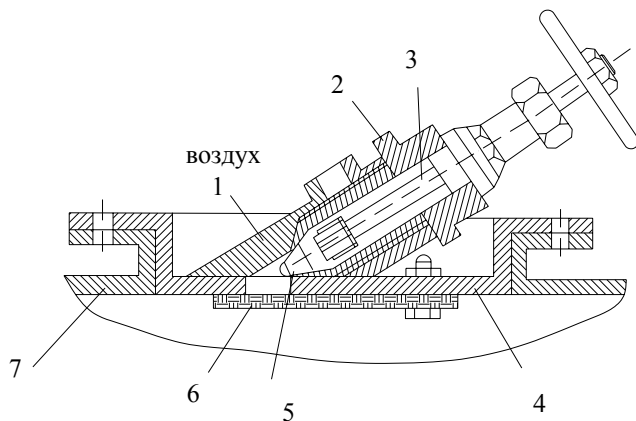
Пневмоэжектор с обратным клапаном для подачи сжатого воздуха в закладочный трубопровод: 1 – патрубок; 2 – конус эжектора; 3 – шток; 4 – стальная пластина; 5 – запорное устройство; 6 – резина; 7 – трубопровод
